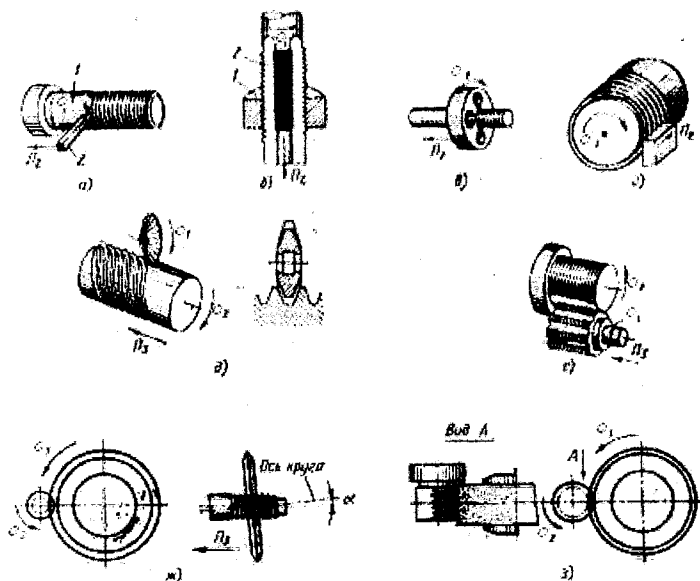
Формоутворення гвинтових поверхонь на заготовках і різальними інструментами 2.
